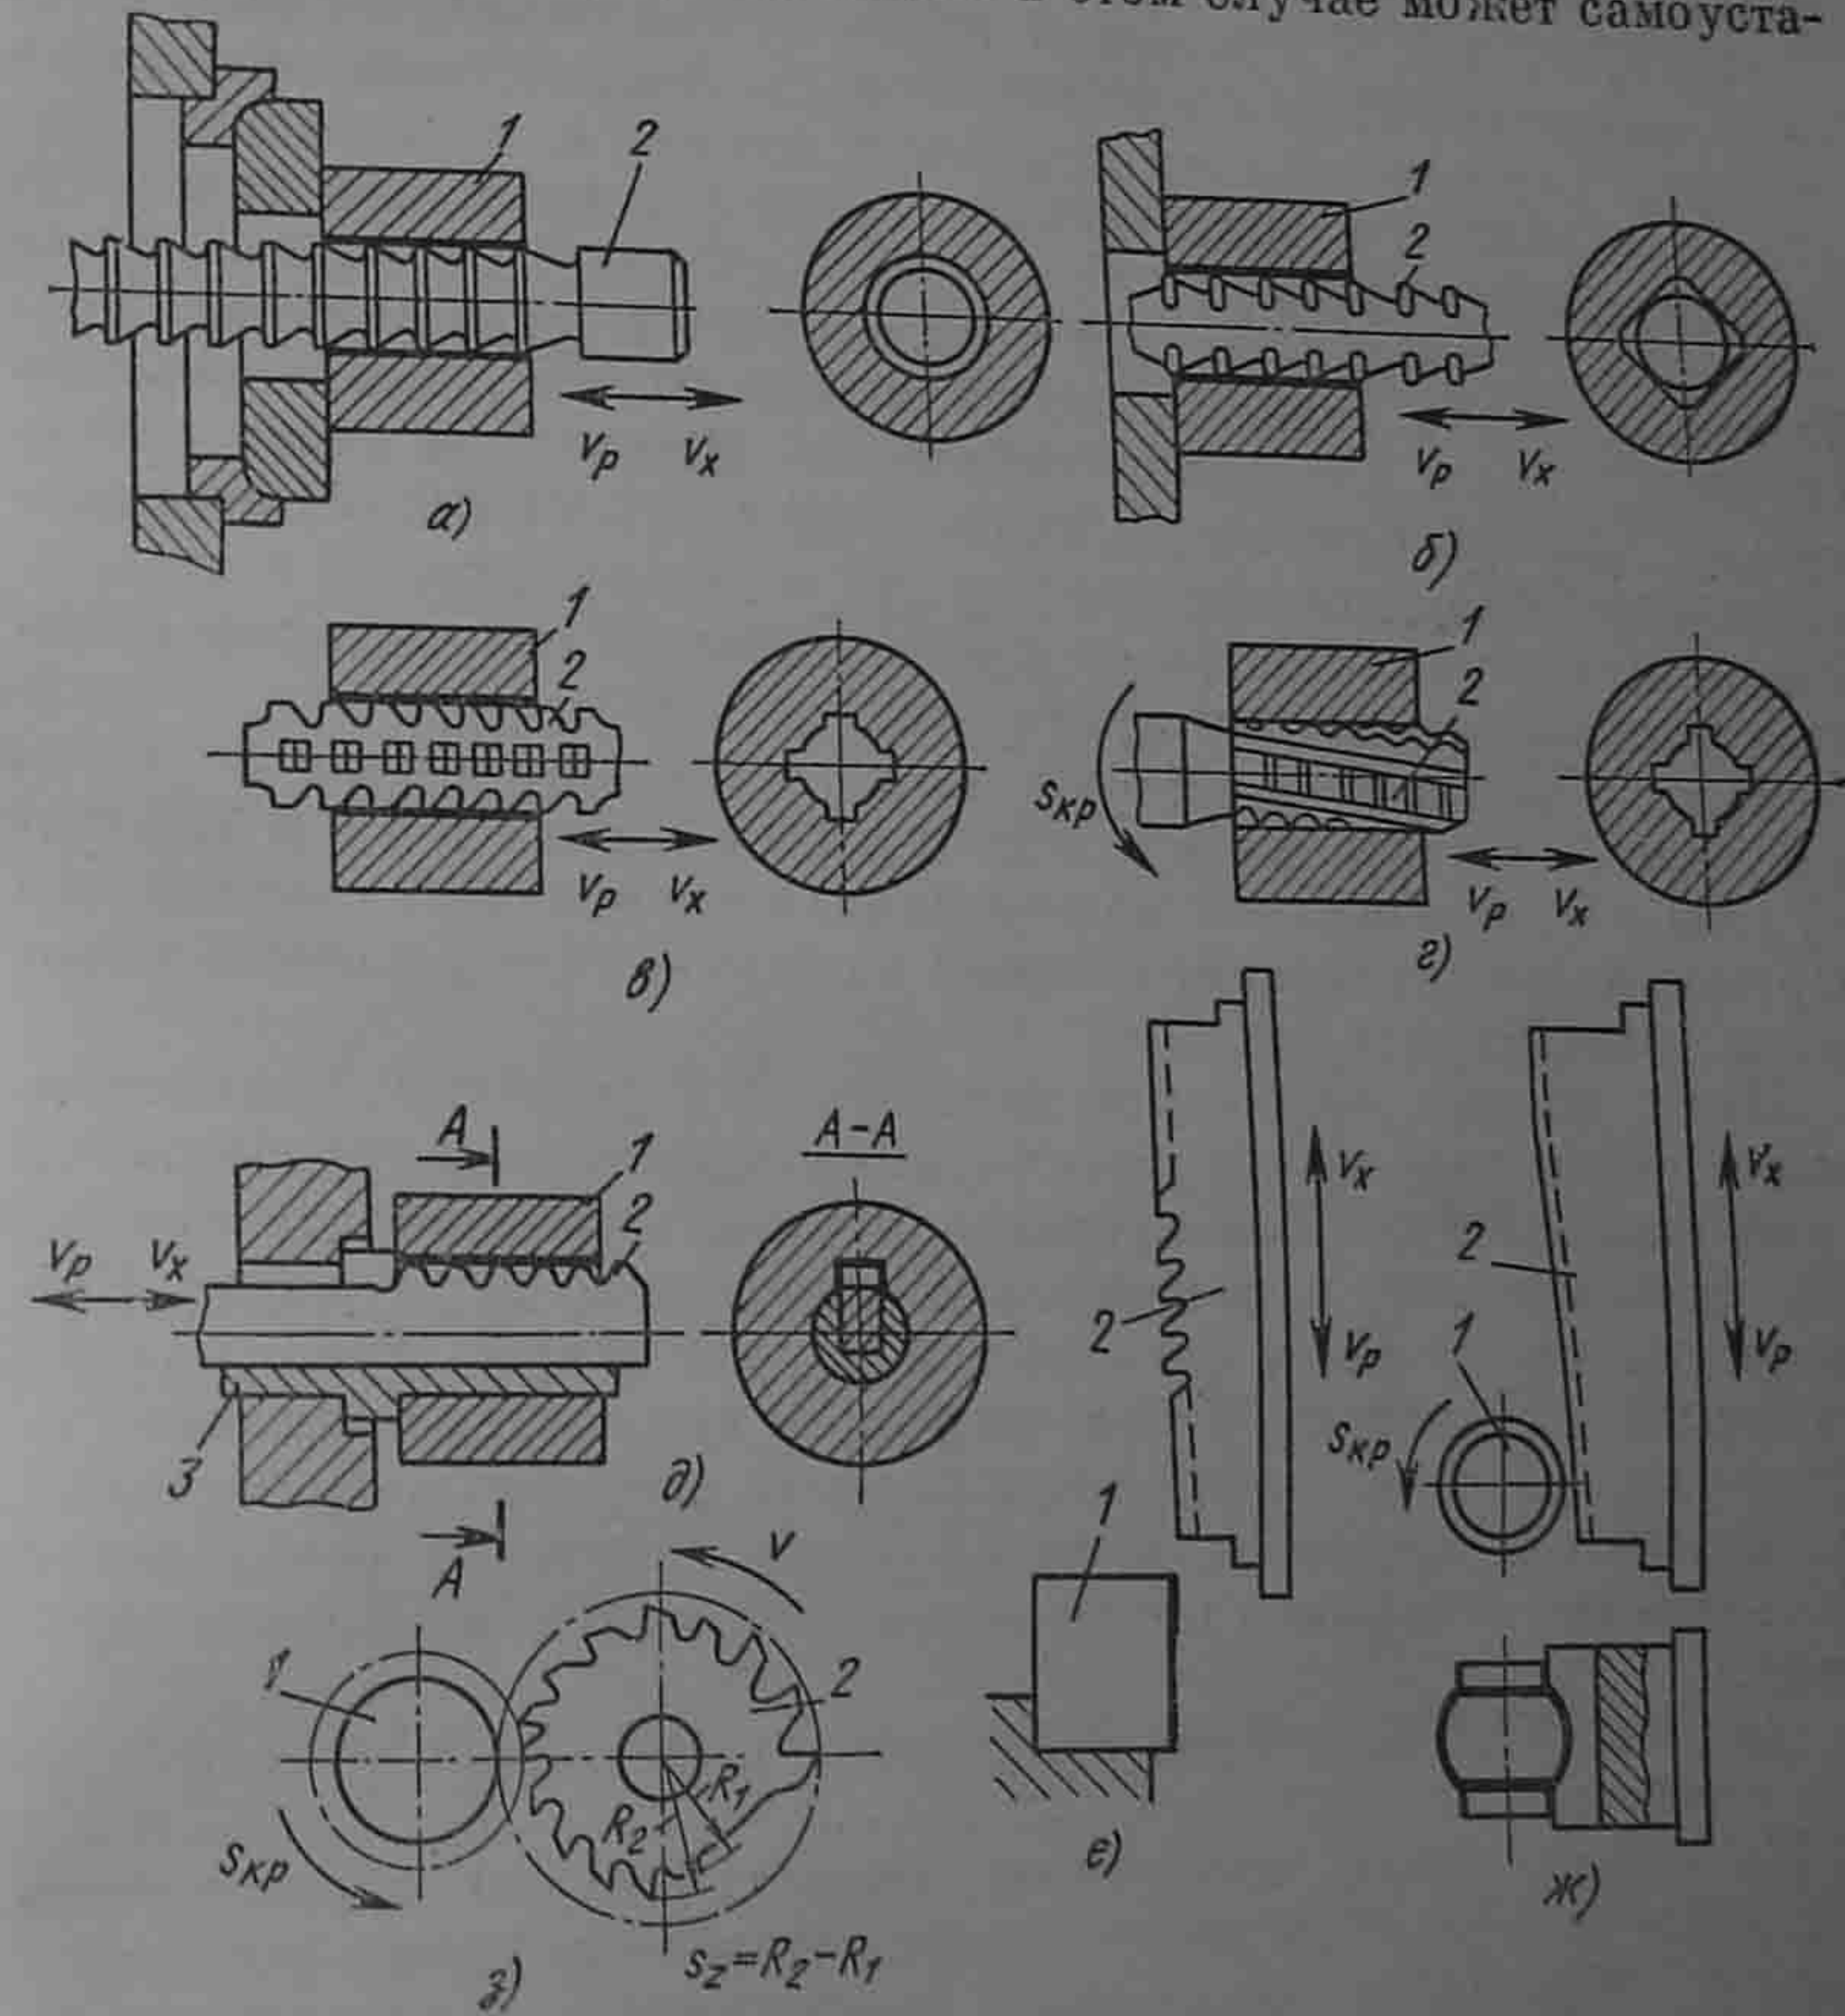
Схемы обработки поверхностей заготовок на протяжных станках: 1 — заготовка; 2 — протяжка; 3 — направляющая втулка
